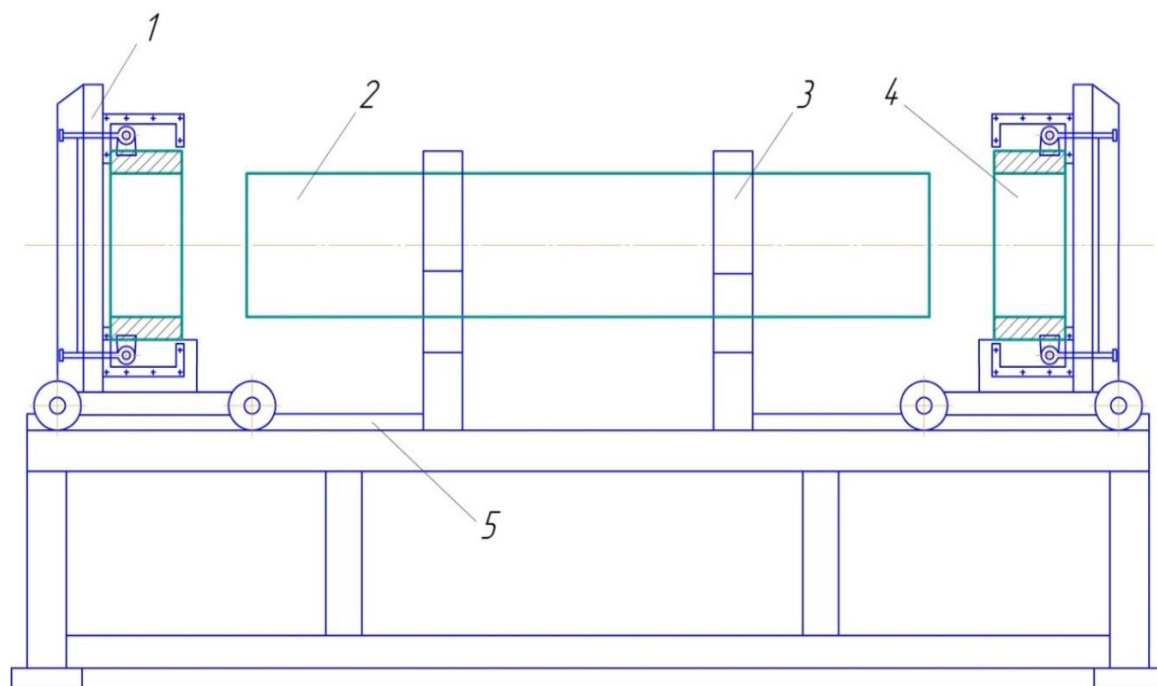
Стенд для сборки гидравлических цилиндров с обсадными кольцами
